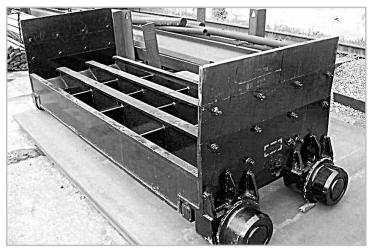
Общий вид прокатно-сварной спекательной тележки
